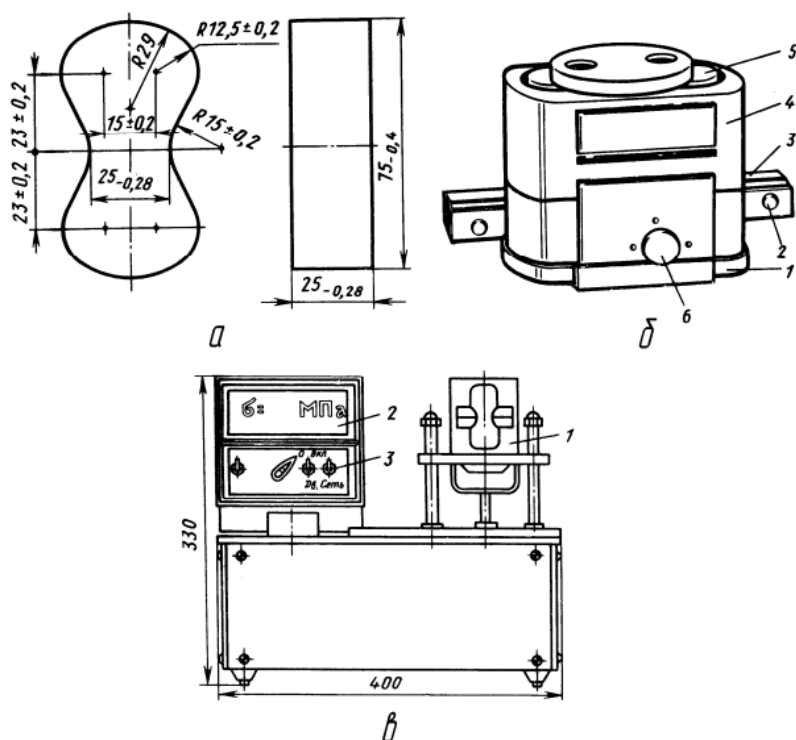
Образец (а), стержневой ящик для его изготовления (б) и прибор модели 04116 для определения прочности образца в сухом состоянии (в)
